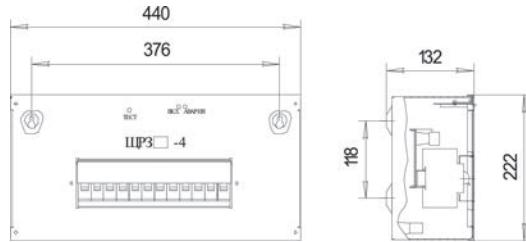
Габаритный чертеж ЩРЗ 24-4(С),
